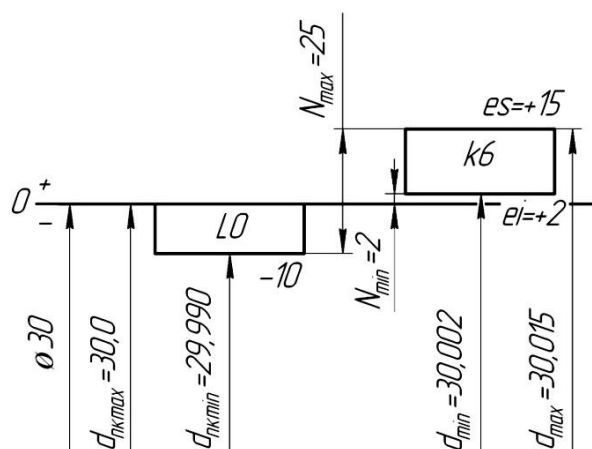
Схема расположения полей допусков сопряжения вал - внутреннее кольцо подшипника
